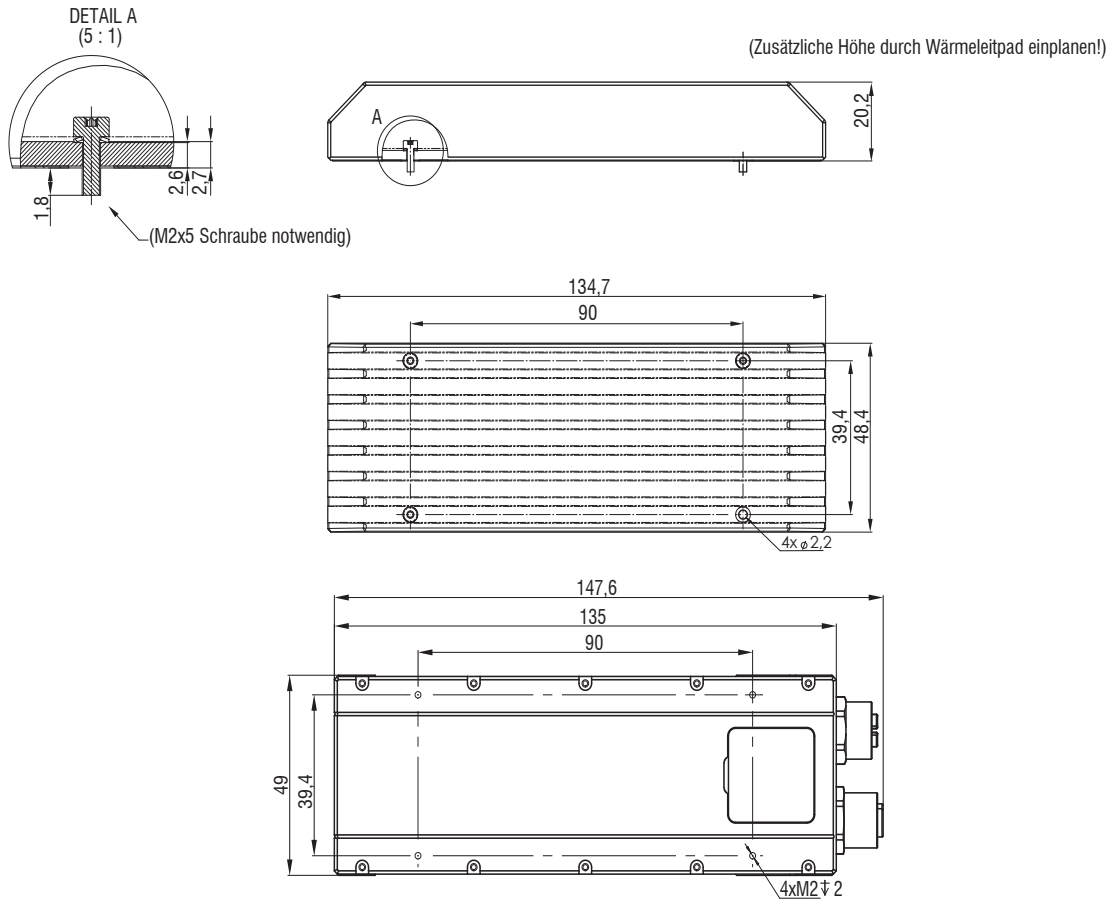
Maßzeichnung Montage Kühlkörper
